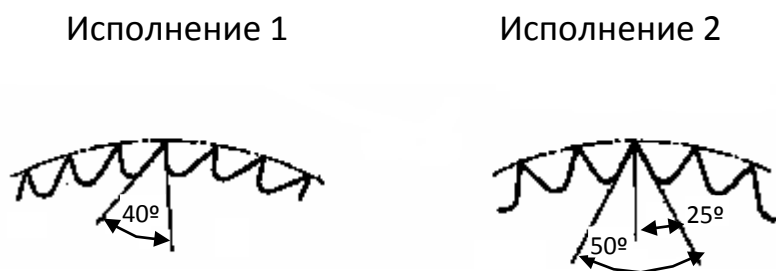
Профили зубьев пил для поперечного пиления древесины
